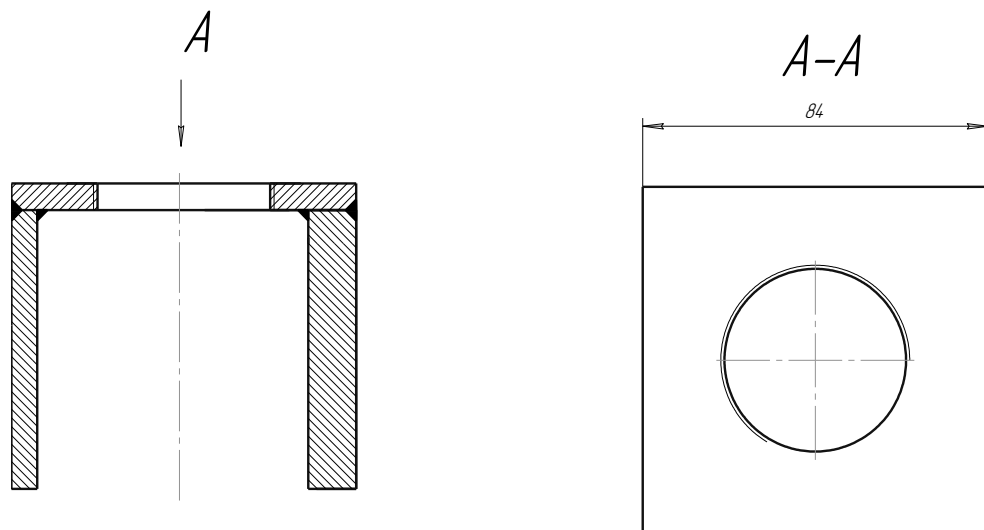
Зварне з'єднання корпусу двигуна
